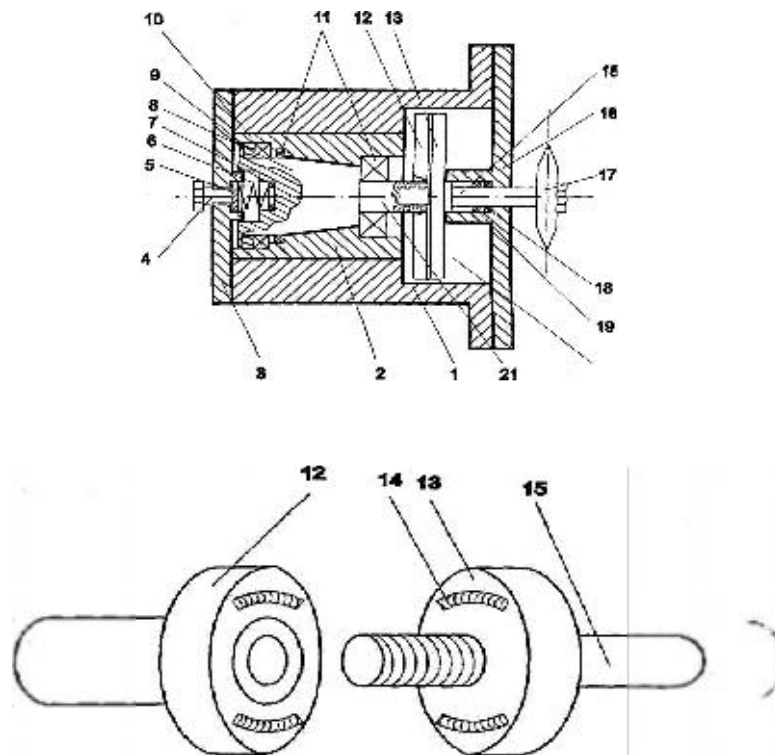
Устройство конусного золотникового механизма газораспределения двигателя внутреннего сгорания
